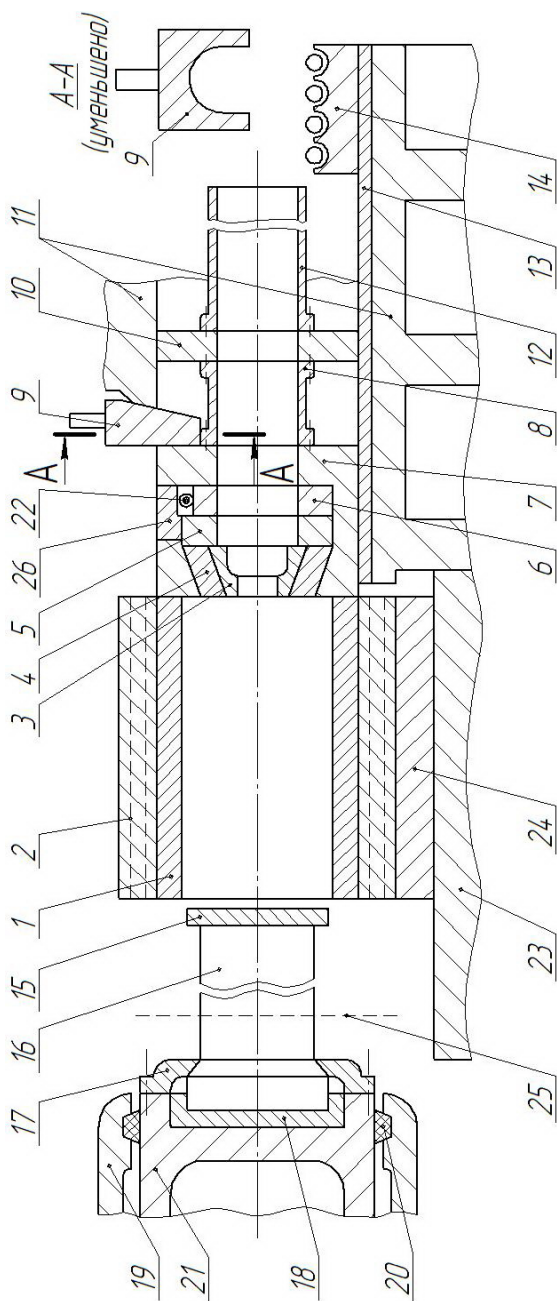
Наладка инструмента для прессования на гидравлическом прессе: 1 – рабочая втулка контейнера;
